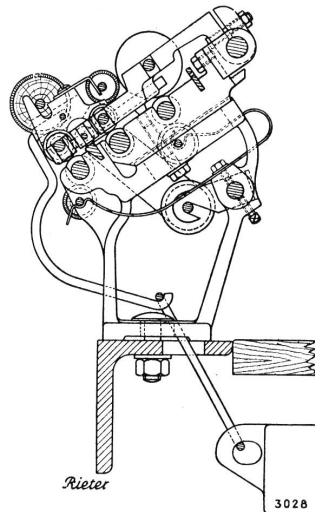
Streckwerk Le Blan-Roth (Schnitt). Aus dem Bild ist das einseitige Laufleder mit Spannrolle deutlich zu erkennen.
